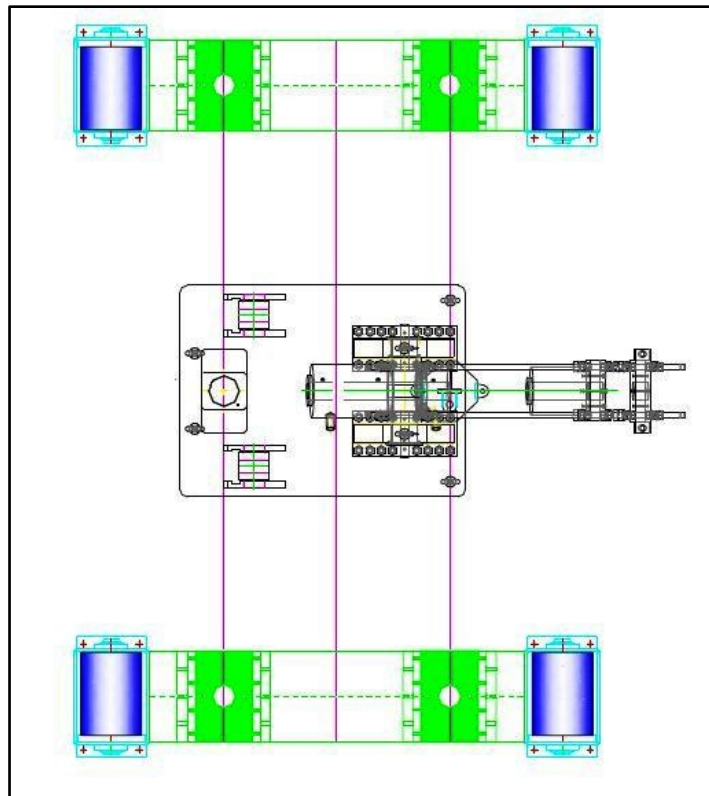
Vista em planta do sistema de movimentação e a sua posição relativamente ao pórtico
